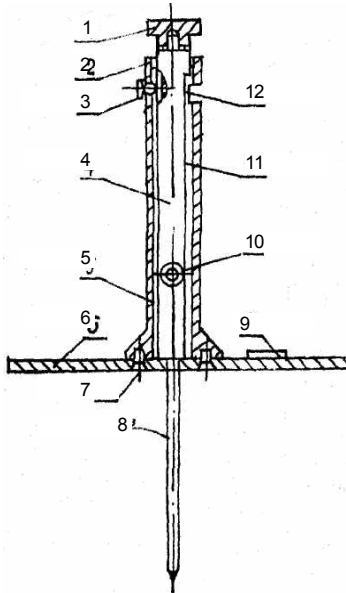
Товщиномір голчастий: 1 — ручка; 2 — втулка; 3 — затисний гвинт; 4 — вставка; 5 — корпус; 6 — основа; 7 — кріпильний гвинт; 8 — голка; 9 — табличка; 10 — кріпильний гвинт; 11 — шкала; 12 — скло
